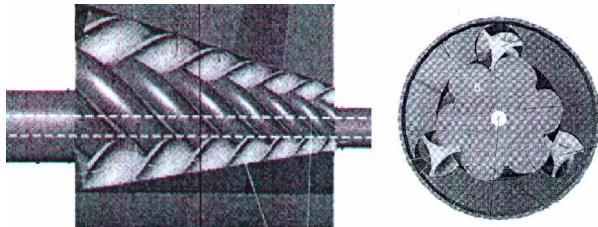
Схема винтового двигателя, его продольный и поперечный разрез
